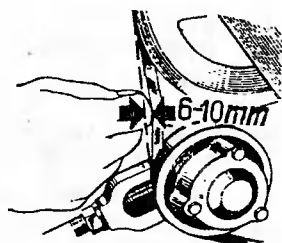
Проверка натяжения ремня компрессора
